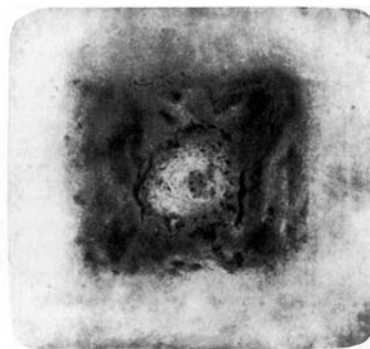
Закалочные трещины, образовавшиеся в заготовке при быстром нагреве
